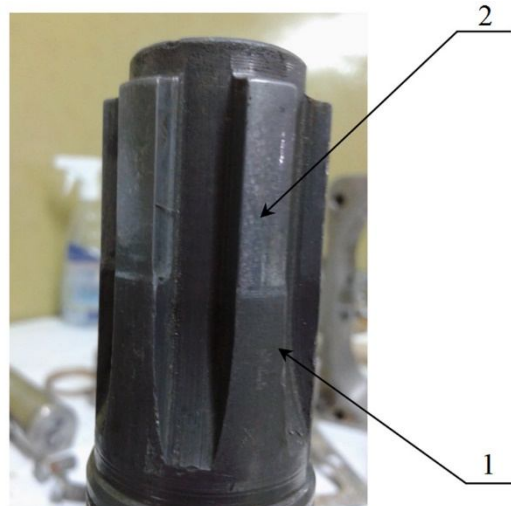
Поверхні ведучого вала: 1 - базова поверхня; 2 - зона зношування
